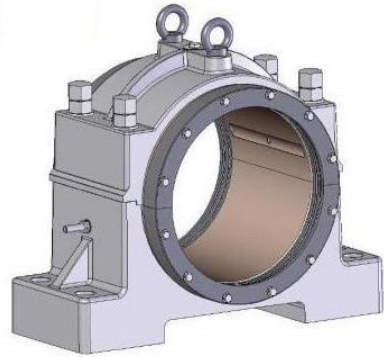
Загальний вигляд підшипника у роз'ємному корпусі
